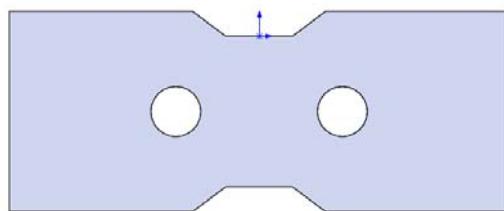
Геометрия образца с дополнительными круговыми концентраторами
